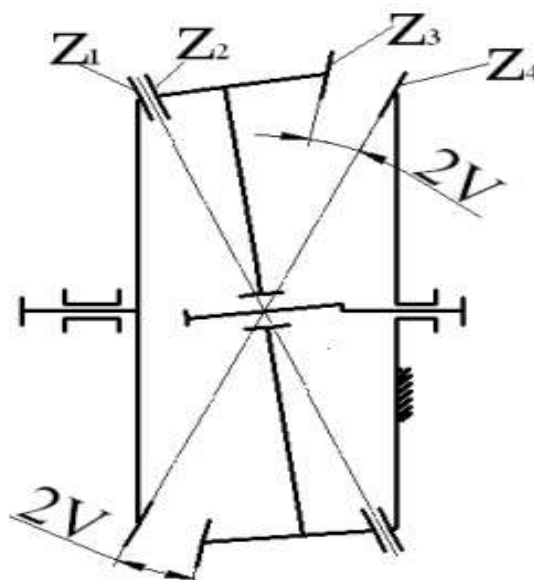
Кинематическая схема двухступенчатого редуктора
